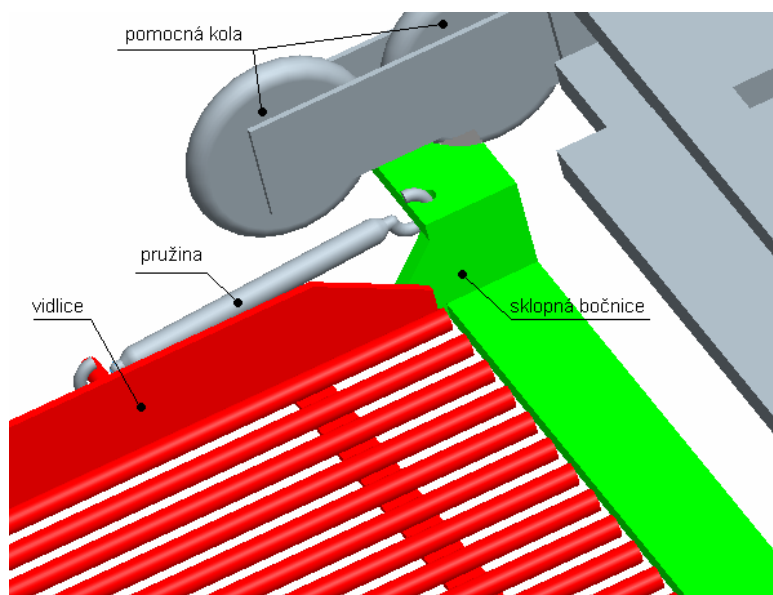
13 Manipulátor s mechanismem s válcovou vačkou (3D pohled)
